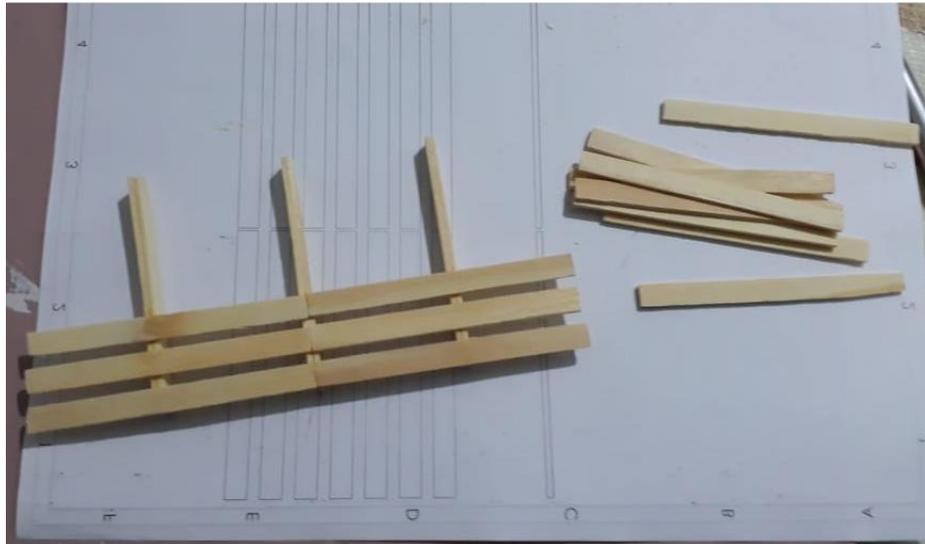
, 25 e 26 – Colagem das peças e aplicação de acabamentos, respectivamente.
